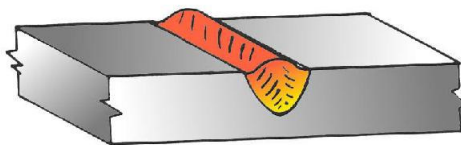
Solda ascendente (6°) em chapa de 12,5 mm
